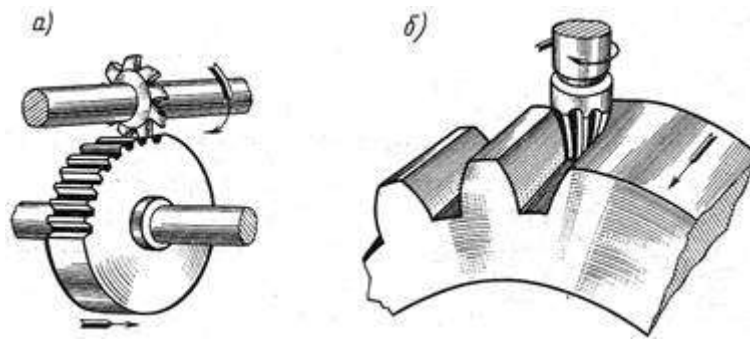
Обработка зубчатых колес методом копирования: а) дисковая фреза; б) пальцевой фрезой
